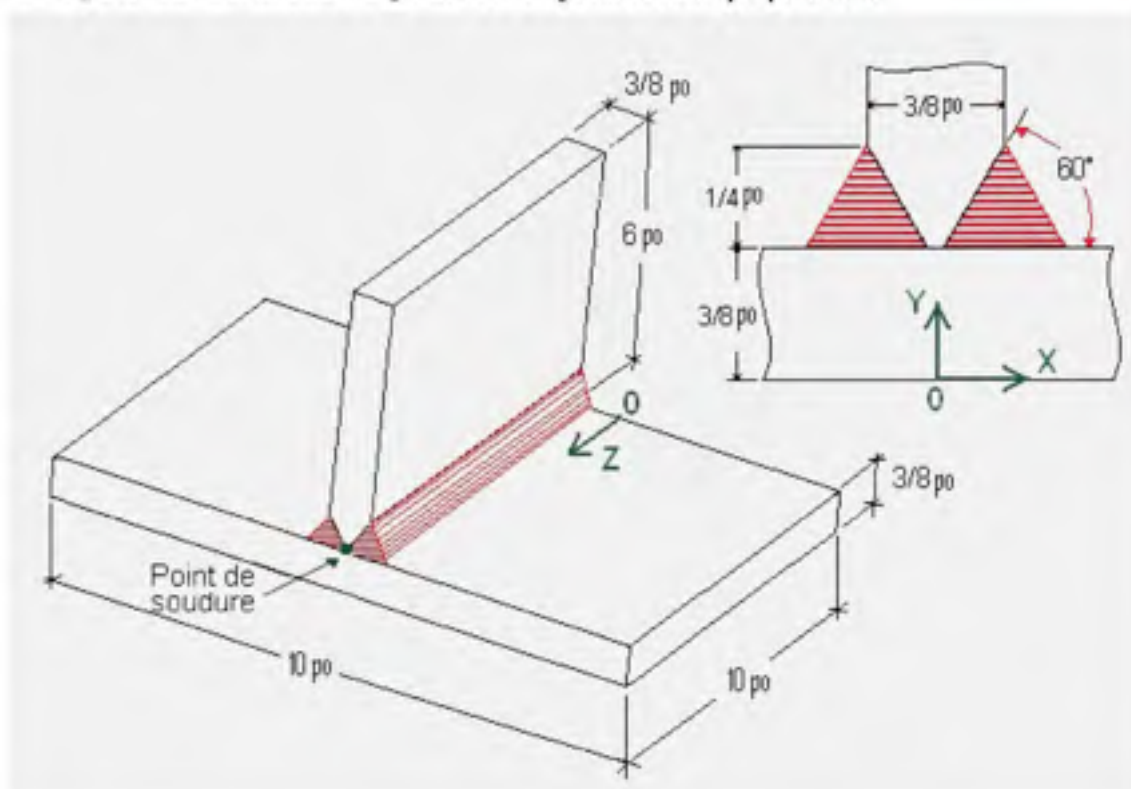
La géométrie des plaques soudées et du joint
